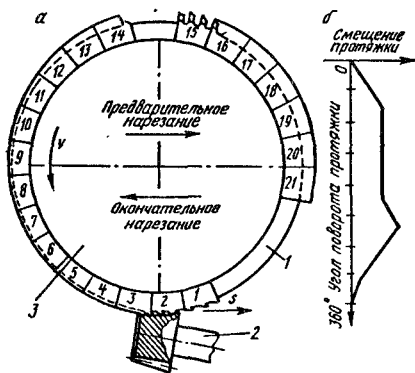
Схема кругового протягивания зубьев конического колеса
